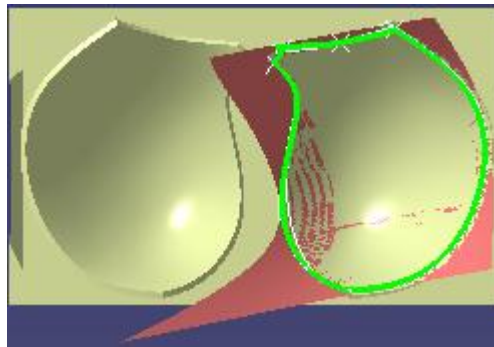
Molde de la talla 115, en el que se inserta la copa de la talla 120
